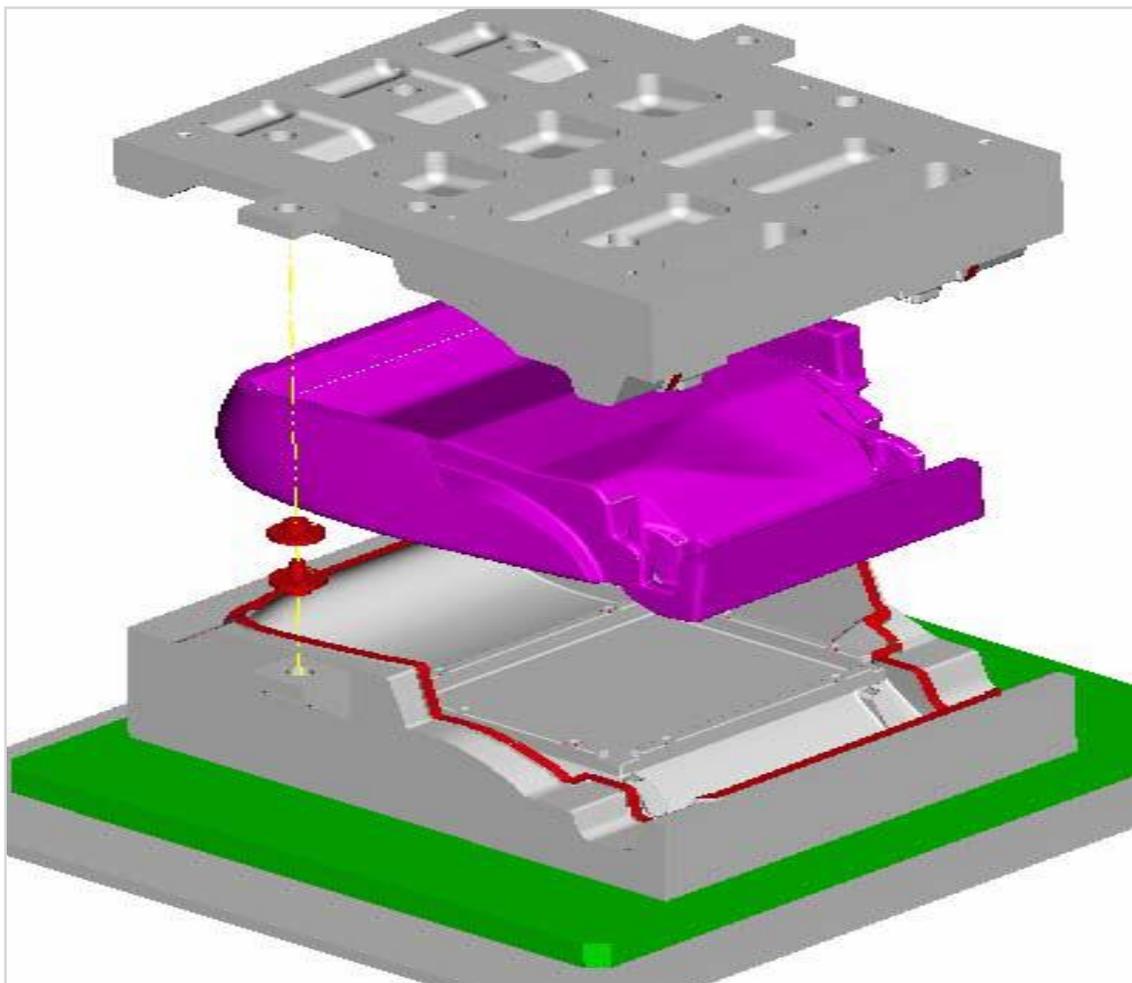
Vista en explosión del conjunto de molde (base y tapa).
